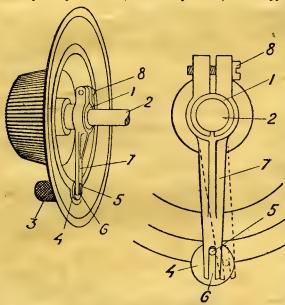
Общий вид и конструкция ручки с подталкивателем.
